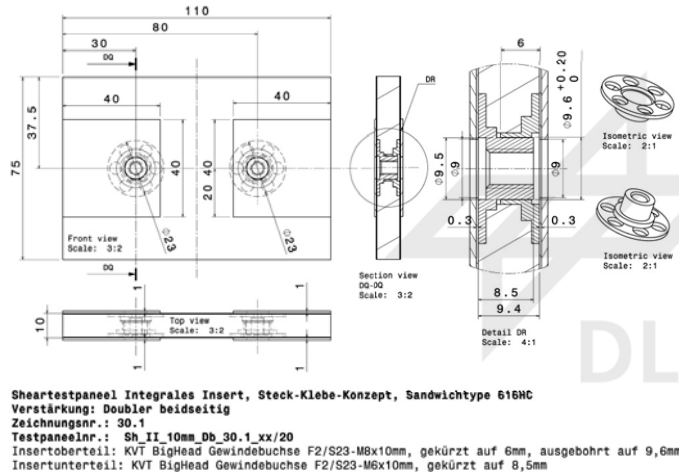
Dimensionen der 616 HC-Sandwichprobekörper inkl. integrierten Inserts (Steckkonzept) für Shear-Versuche, Beispiel mit beidseitiger Deckschichtverstärkung.
